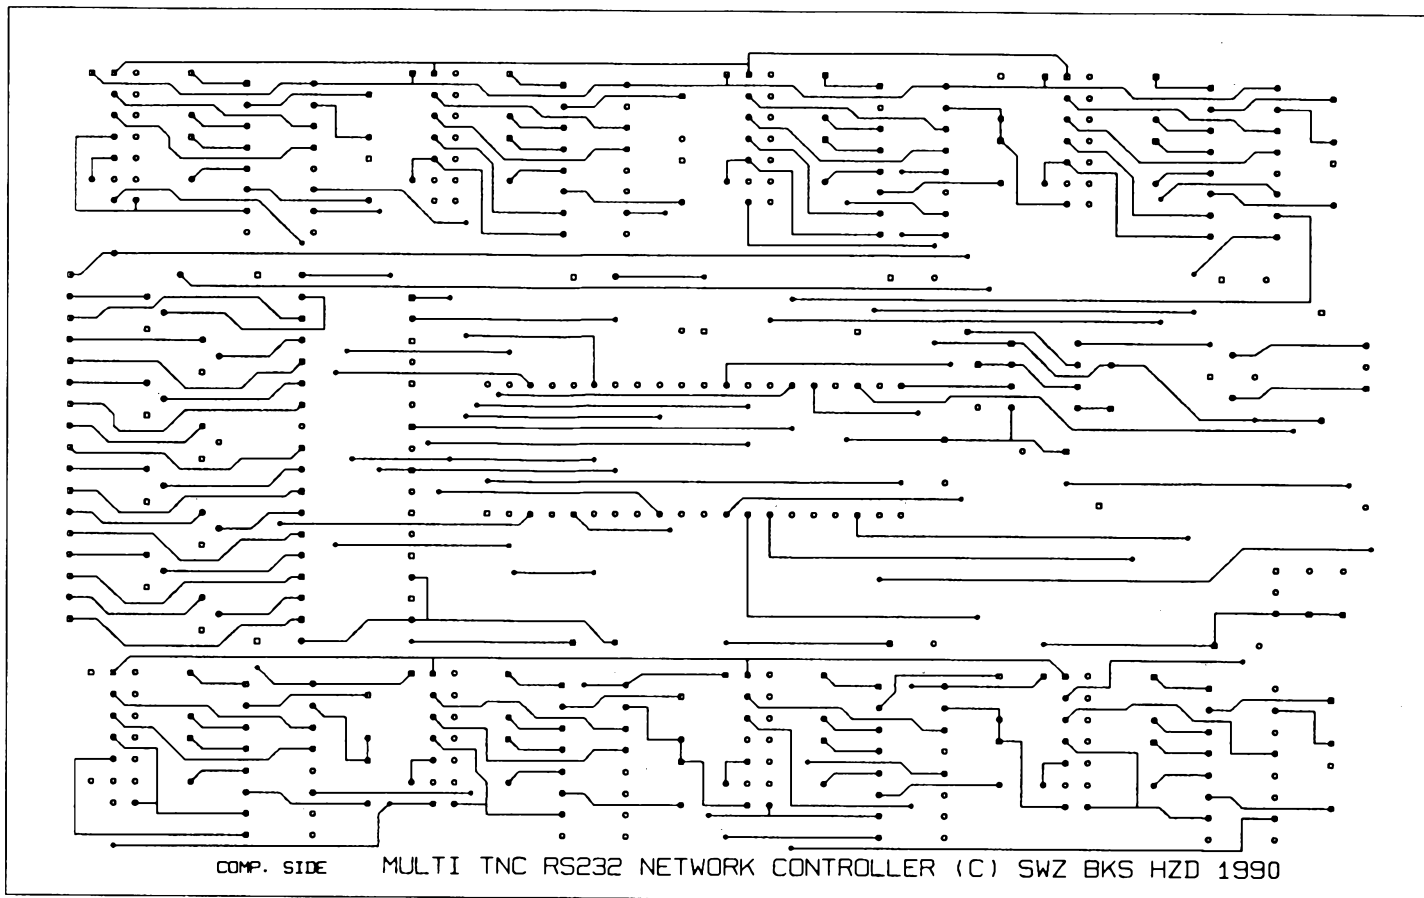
PCB layout knooppuntregelaar, componenten zijde.
